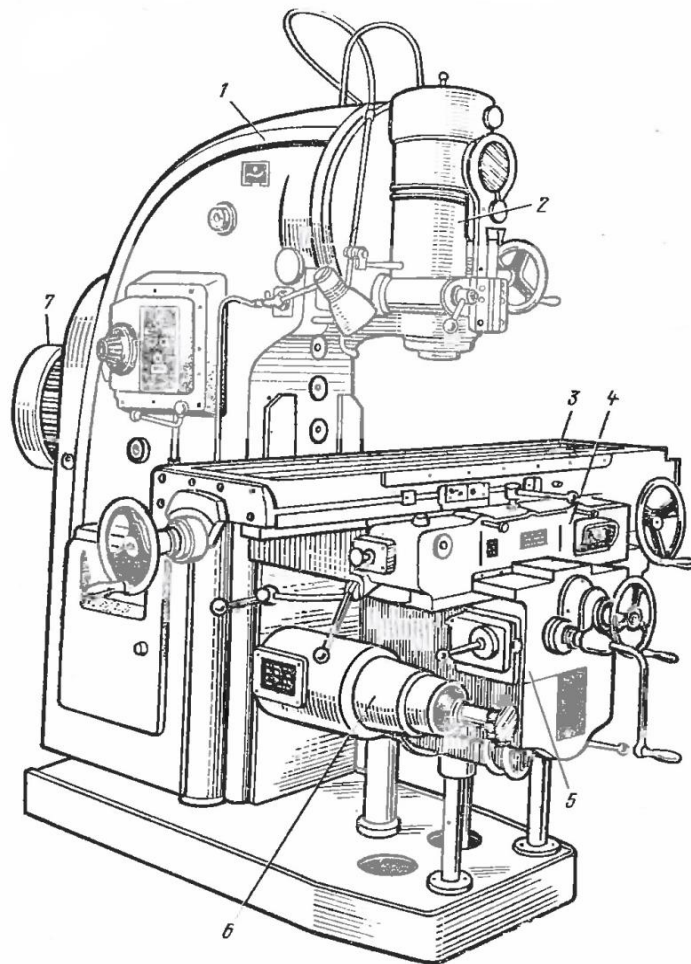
Вертикально-фрезерный станок модели 6Н13
